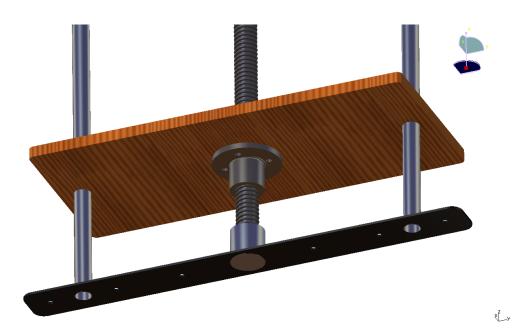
Renderização do atuador vertical levemente estendido 40 mm
